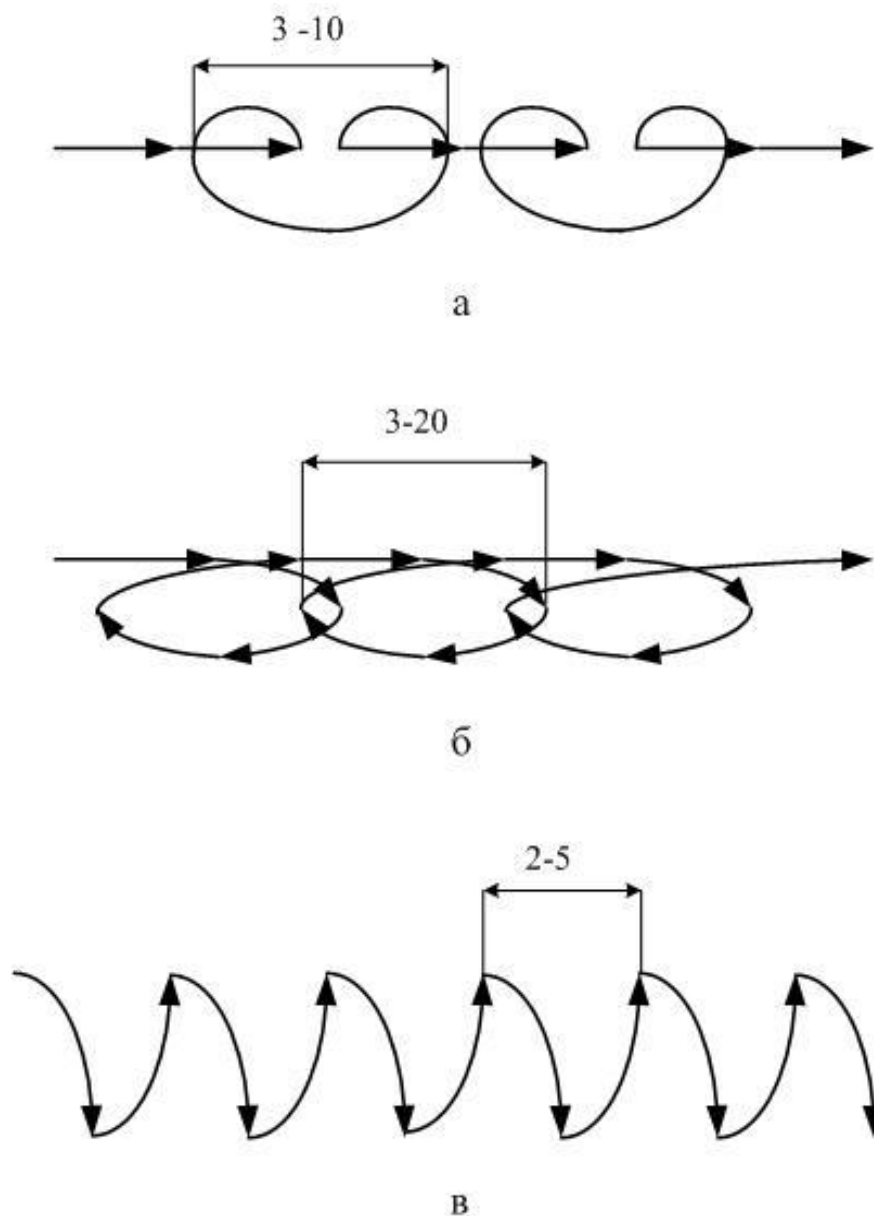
Схемы перемещения электрода при сварке плавящимся электродом в защитных газах для увеличения ширины шва: а и в – для получения равномерного провара по всей ширине шва, б – для получения плавного перехода от усиления шва к основному металлу на одну сторону от его продольной оси.
